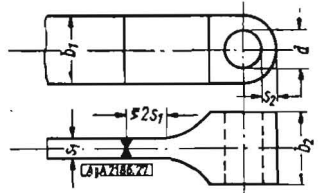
Ähnliche, doch vereinfachte Ausführung wie in Bild 27. Nur für Schmelzschweißung geeignet; kommt größtenteils für Einzelfertigung in Betracht
